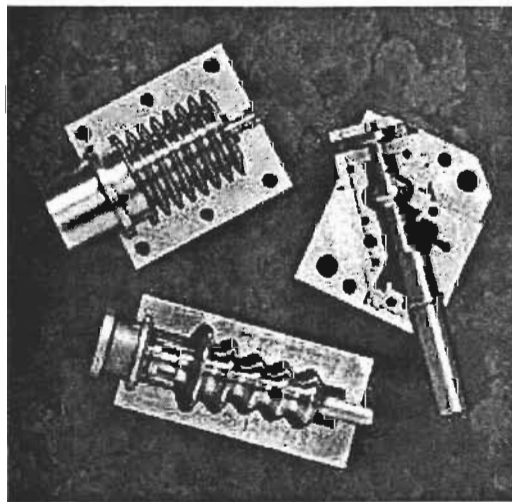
Aspecto de moldes para transformar hule por compresión.
